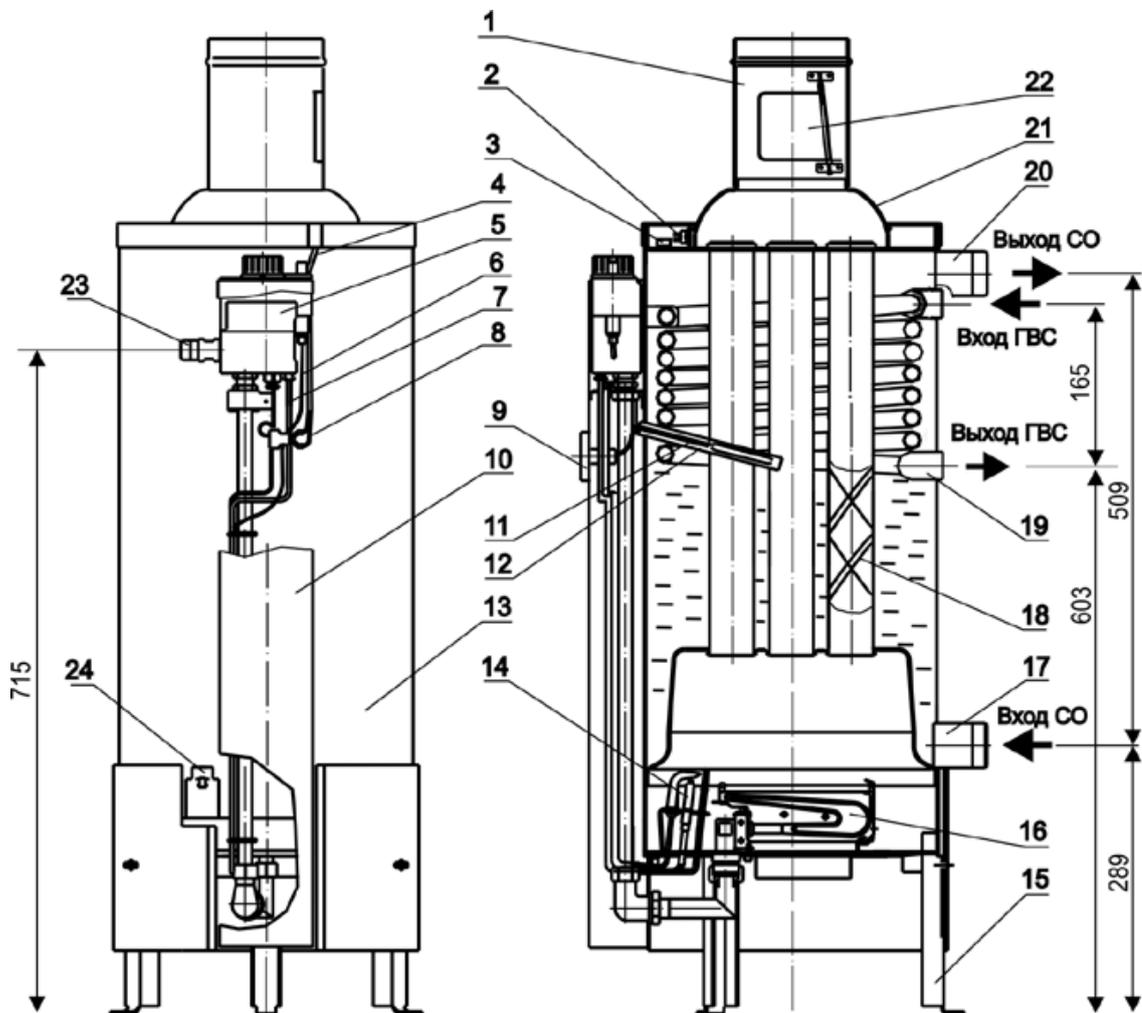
Котел отопительный газовый бытовой напольный комбинированный КОГБК-11,6 EUROSIT
